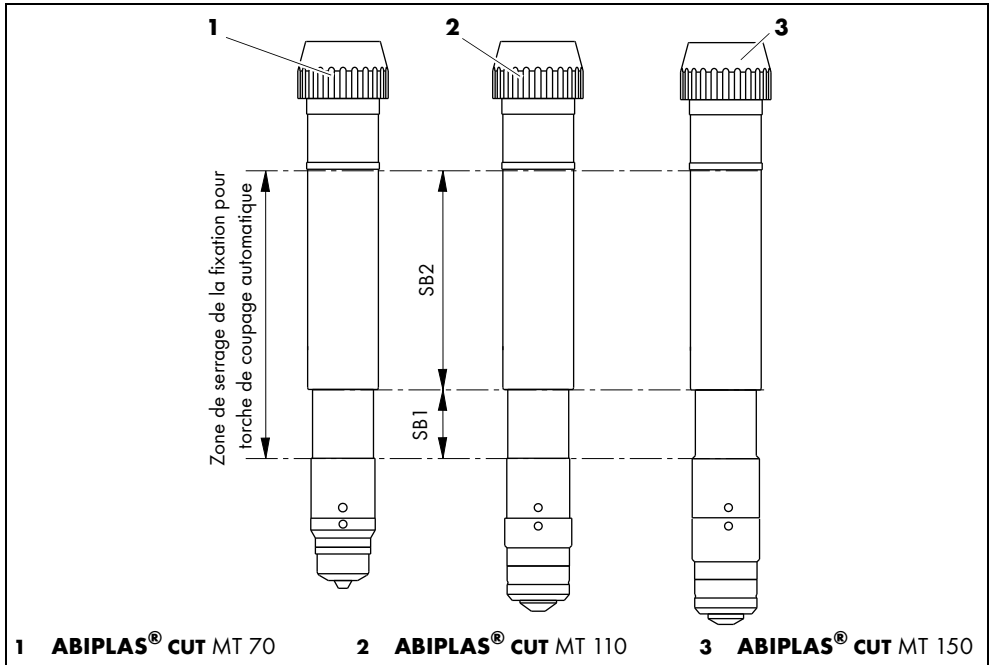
Vue d'ensemble de ABIPLAS® CUT 150
